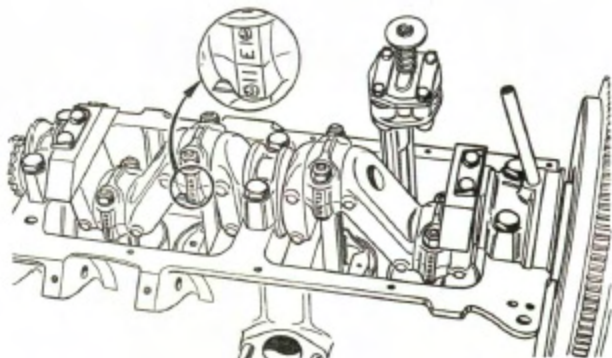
Vue de dessous d'un cylindre (carter inférieur enlevé)
